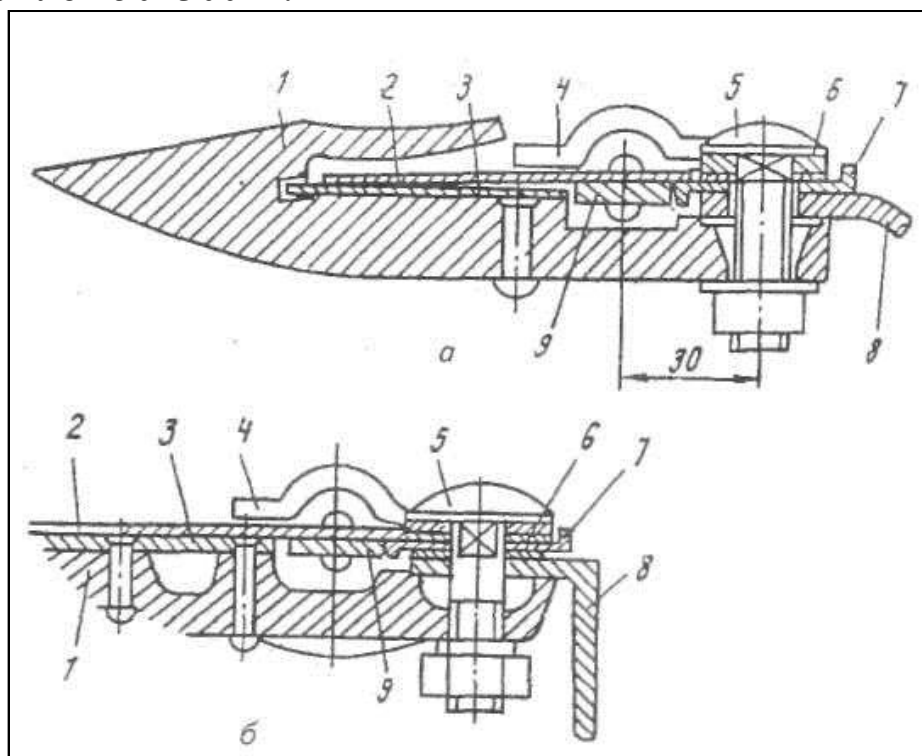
Режущий аппарат: а – перьевой; б – бесперьевой (открытый); 1 – палец; 2 – сегмент; 3 – противорежущая пластина; 4 – прижим; 5 – болтовое соединение; 6 – регулировочная прокладка; 7 – пластинка трения; 8 – передний брус жатки; 9 – режущая пластина (нож)
